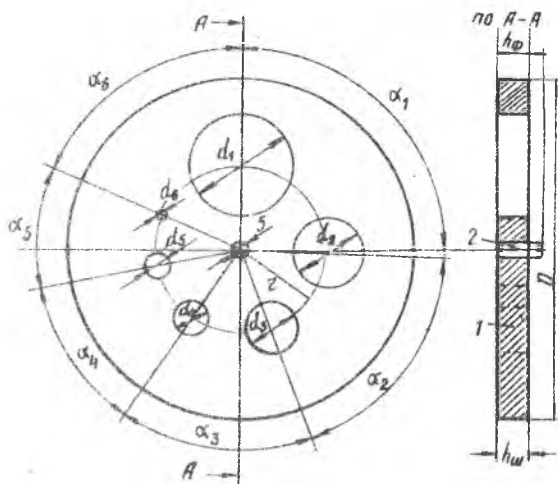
Экспериментальная матрица для пробивки круглых отверстий
